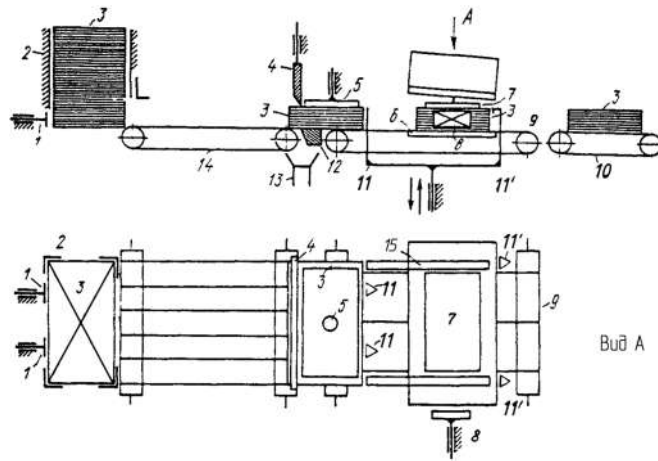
Принципова технологічна схема різальної машини для заготовок упаковки двопозиційної трьохножової: 1 - штовхач заготовки; 2 - магазин заготовок; 3 - книжковий блок; 4 - ніж передній; 5 - притискач заготовки; 6 - ніж жорстко закріплений; 7 - фінальний притиск; 8 - штовхач; 9 - конвеєр; 10 - транспортер; 11 - упор; 12 - жорстко закріплений ніж; 13 - лійка; 14 - транспортер стрічковий; 15 - бічні ножі
